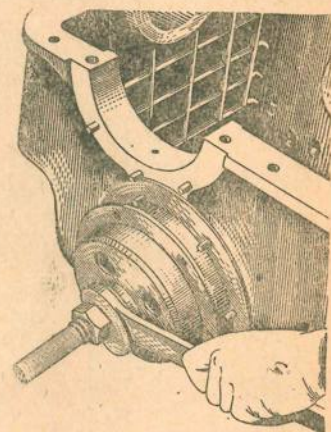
Запрессовка обоймы главного вала в картер коробки перемены передач
